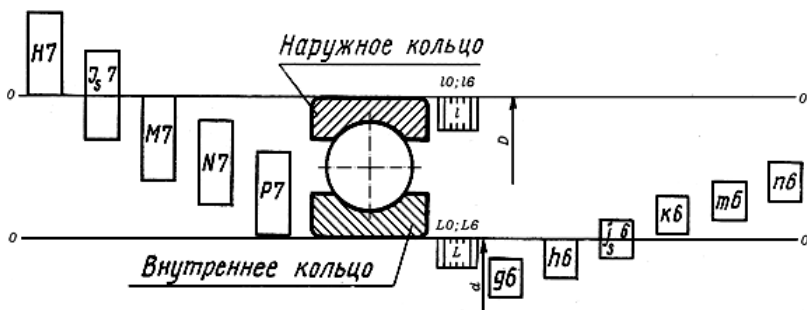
Схема относительного расположения полей допусков колец подшипников
